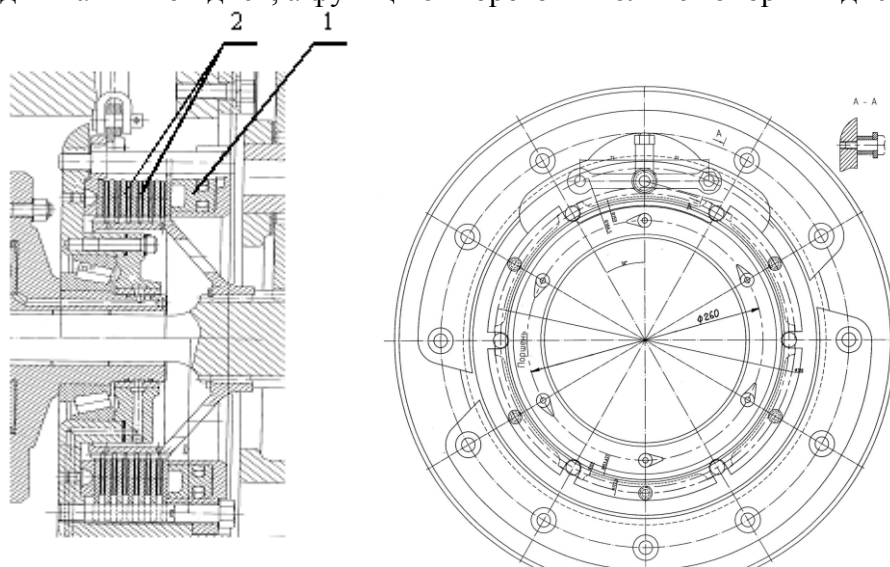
Предлагаемая конструкция тормозного механизма
